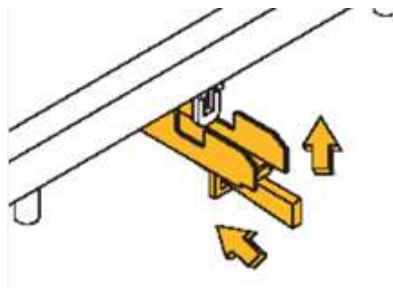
Demonstração da colocação dos cabeçais nas longarinas
